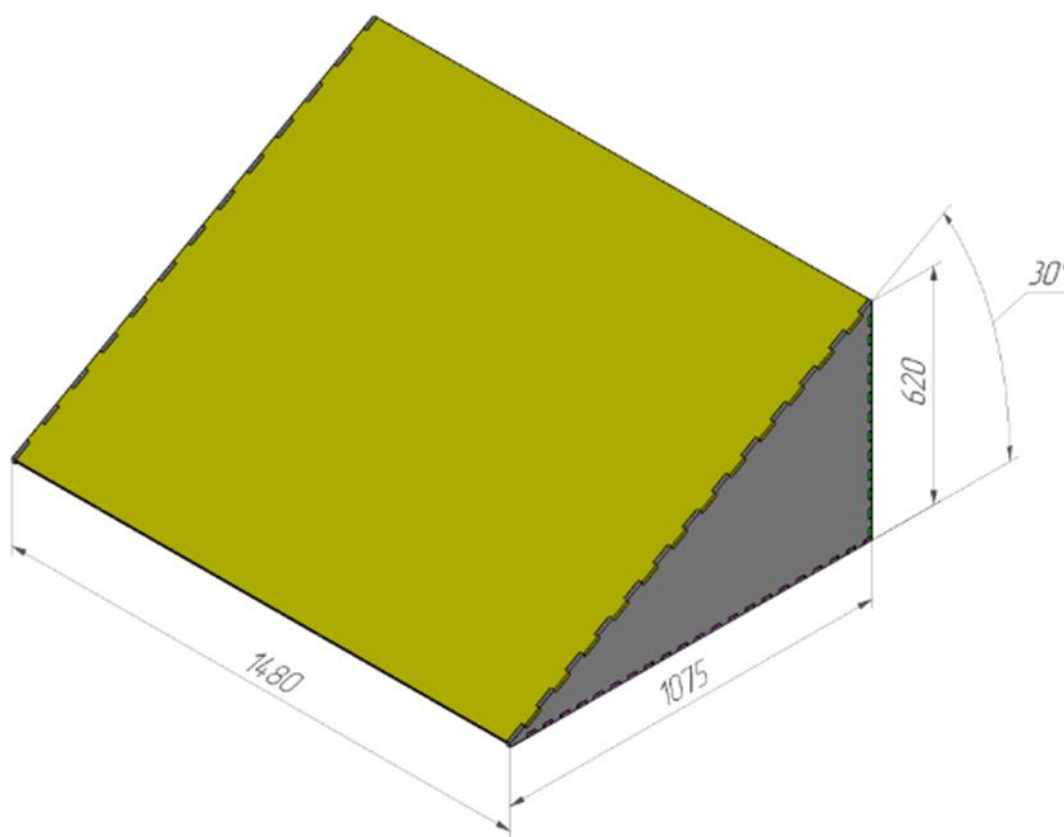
Наклонная поверхность 30 (габаритные размеры)
